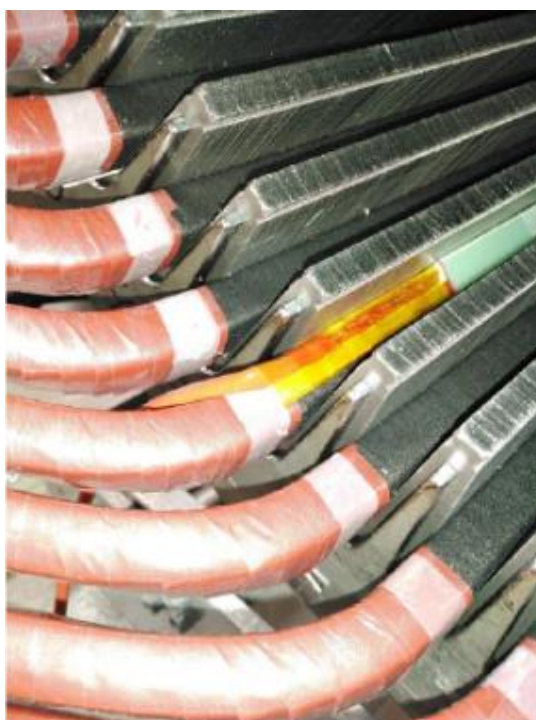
Sensor Pt100 inserido na bobinagem estatórica.
